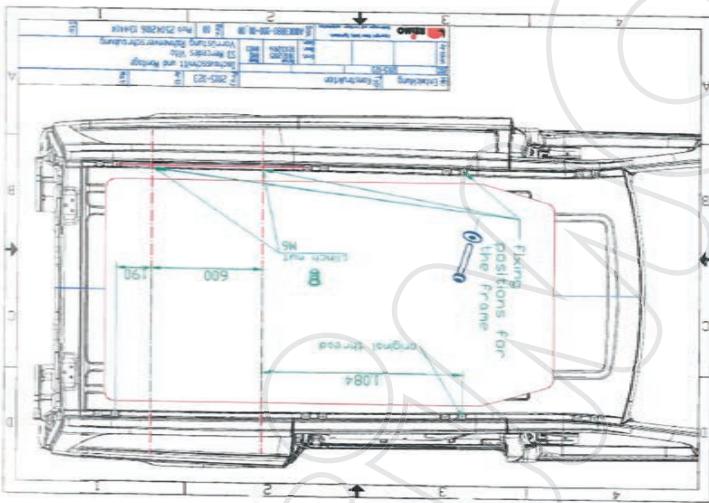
Zeichnung Dachausschnitt 2
